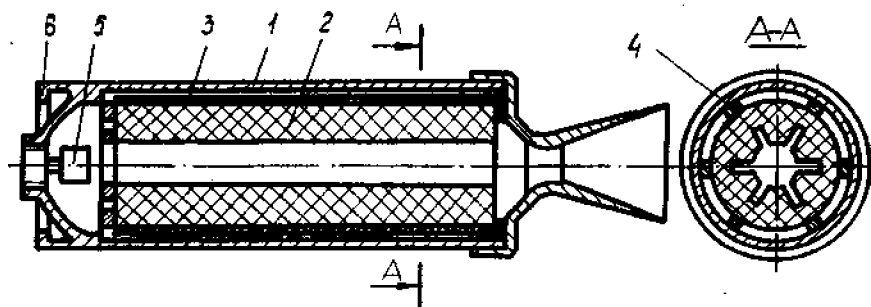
Схема РДТТ с вкладным зарядом: 1- корпус; 2 – заряд;
